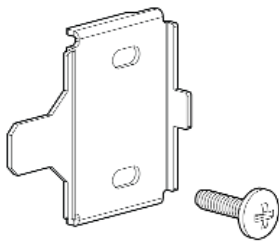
Eindreihen der Schraube in die neue Halterung
